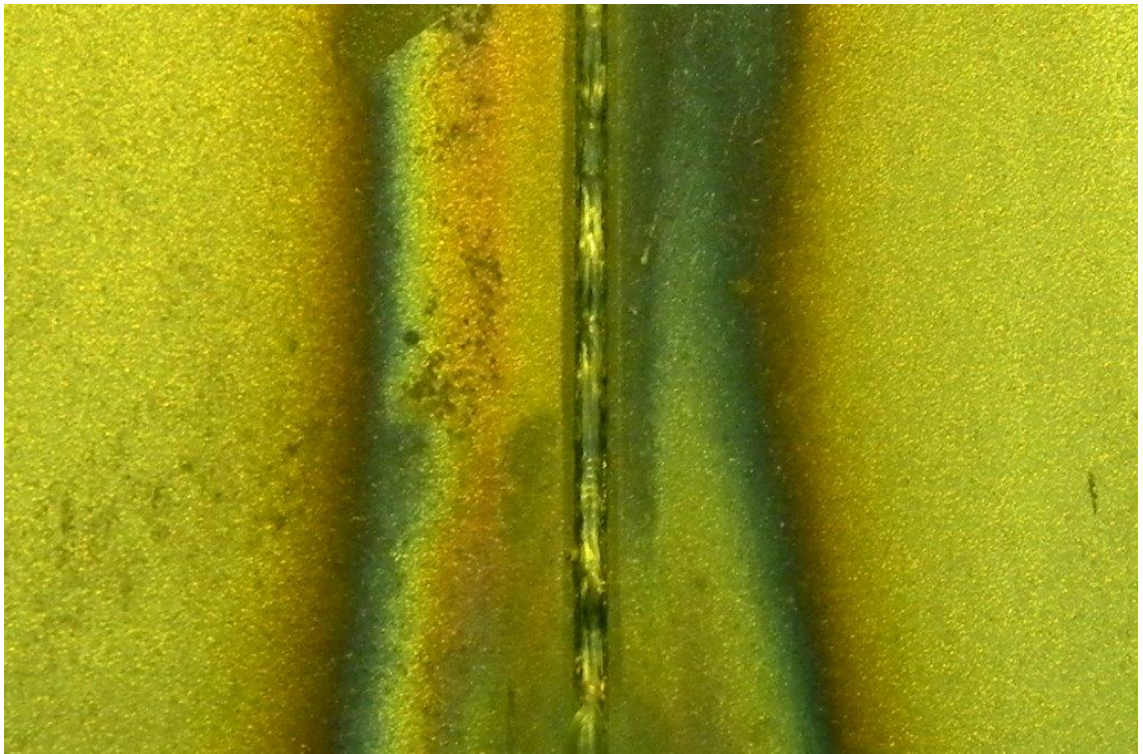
Образец после сварки подготовленный лазерной резкой с EPS
